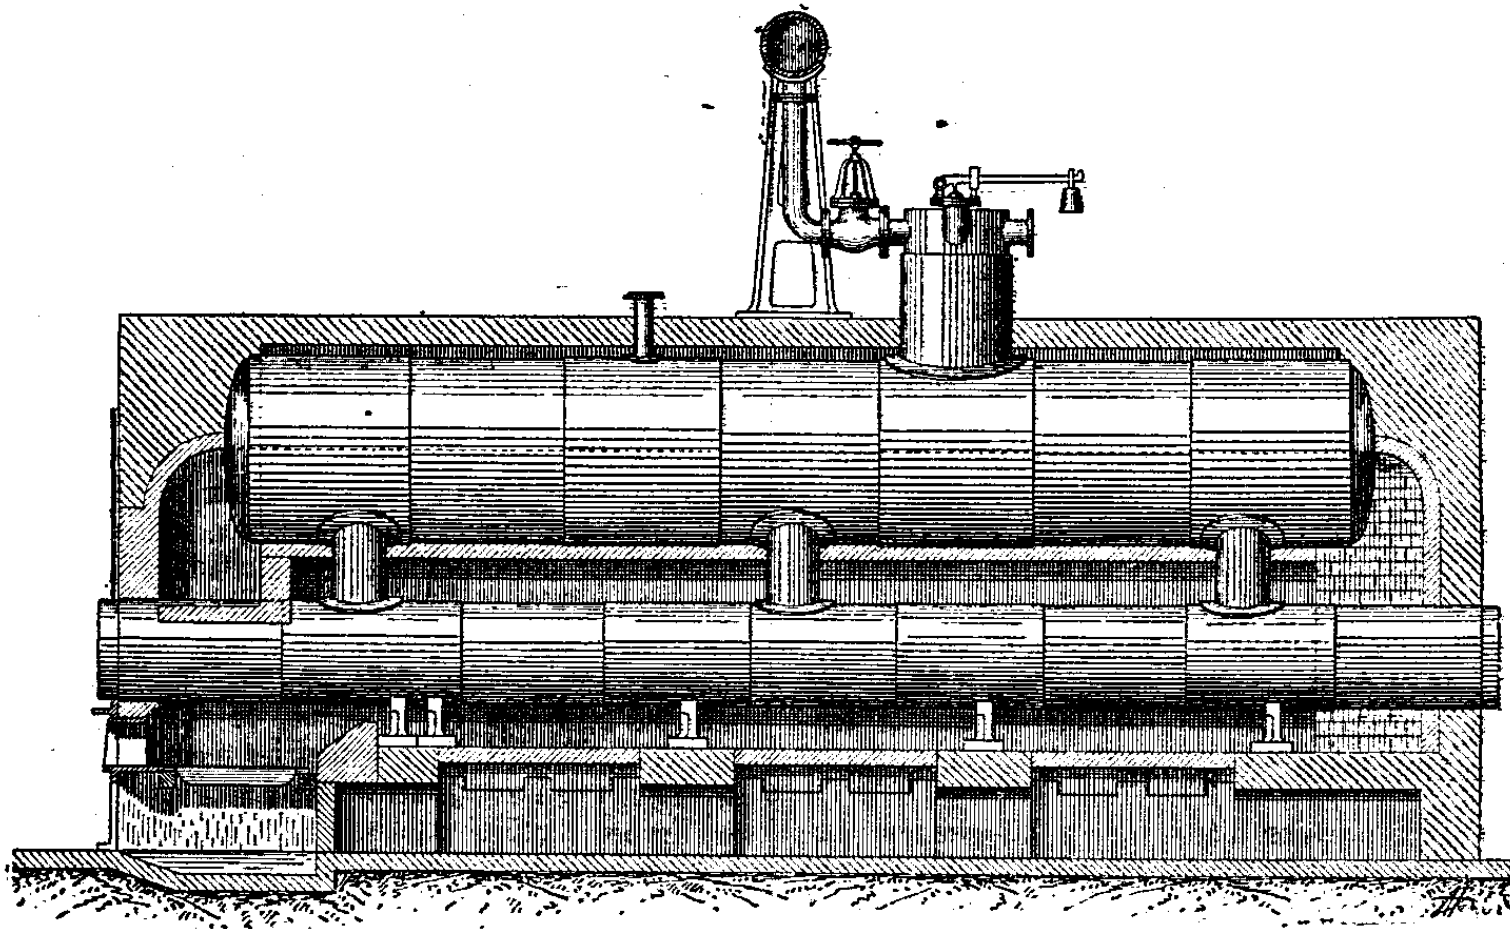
Coupe longitudinale d'une chaudière à bouilleurs.
